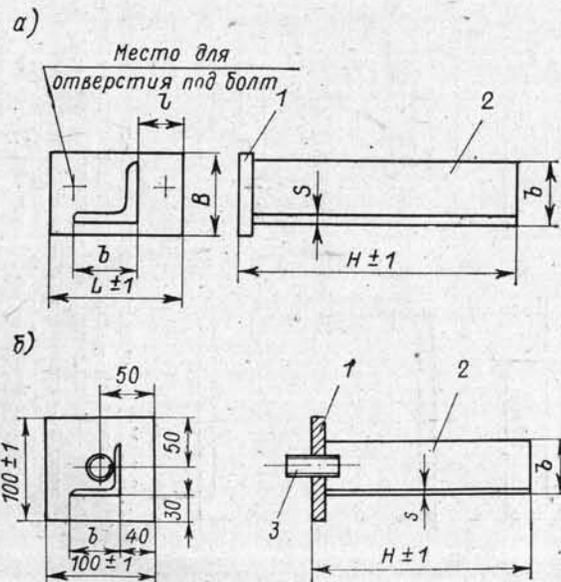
Стойки под амортизаторы: а — для помещений без зашивки изоляции; б — для помещений с зашивкой изоляции.
